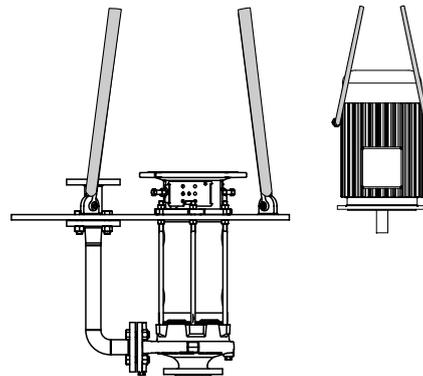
Pumpe und Motor ab Motorbaugröße 180 getrennt transportieren
